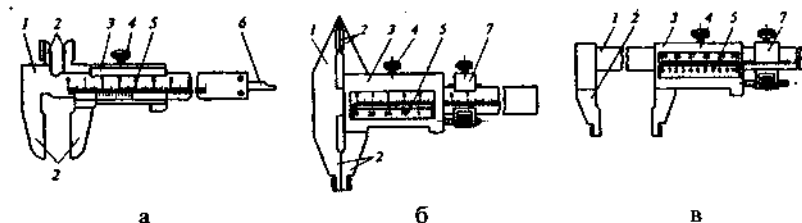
Конструкции штангенциркулей: а – тип ШЦ-I; б – тип ШЦ-II; в – тип ШЦ-III; 1 – штанга-линейка; 2 – измерительные губки; 3 – рамка; 4 – винт зажима рамки; 5 – нониус; 6 – линейка глубиномера; 7 – рамка микрометрической подачи
